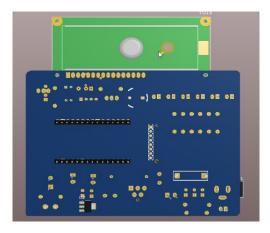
Sơ đồ mạch in PCB mạch Master
